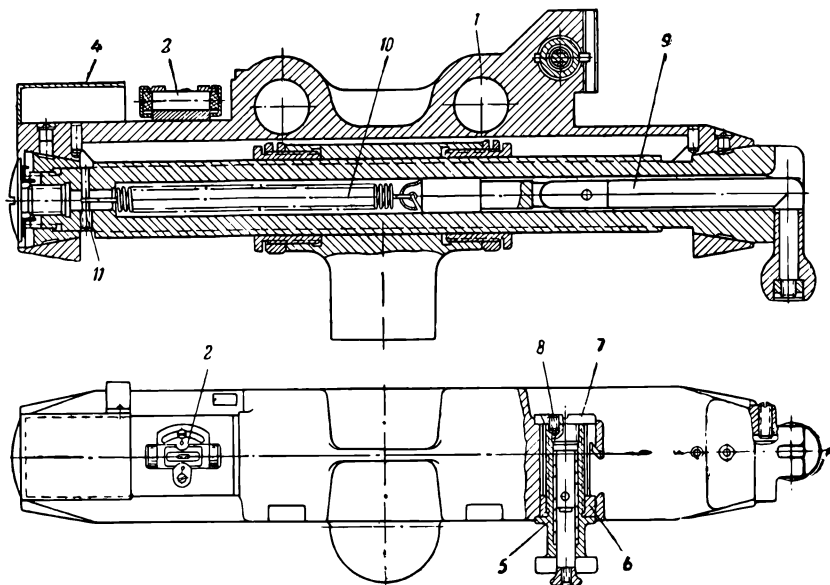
Вертлюг 120-мм миномёта обр. 1938 г. с поворотным механизмом старого изготовления:
